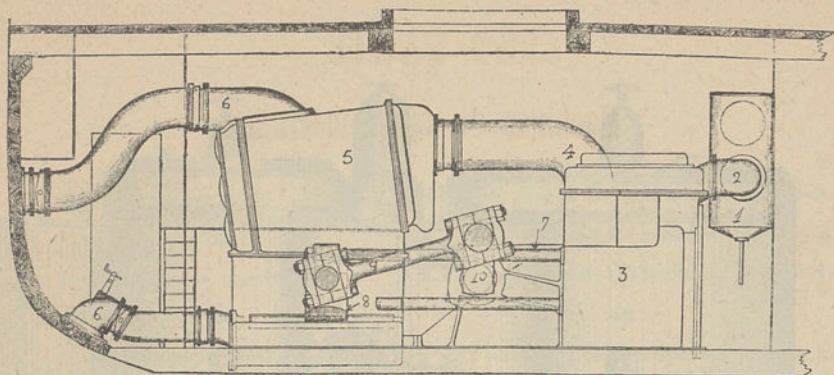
MACHINA DE CYLINDRO OSCILANTE. (Propulsor, rodas)
